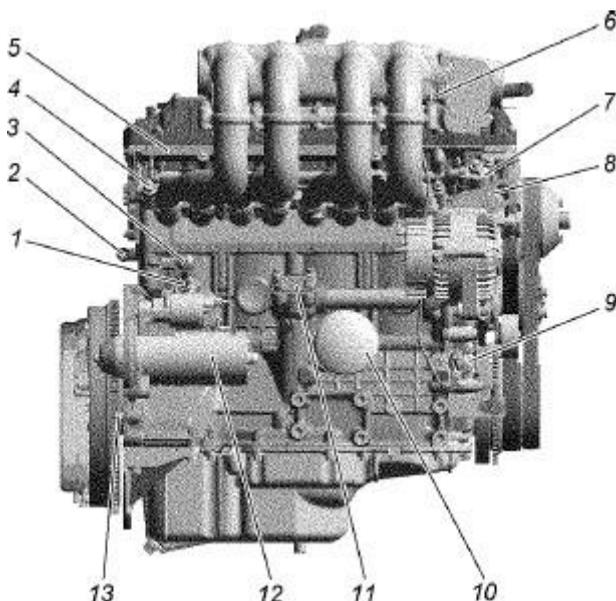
Motor ZMZ-409051 (vista derecha):
